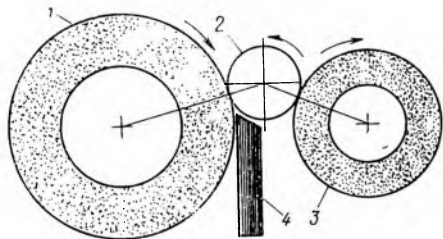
Схема круглого наружного бесцентрового шлифования:
